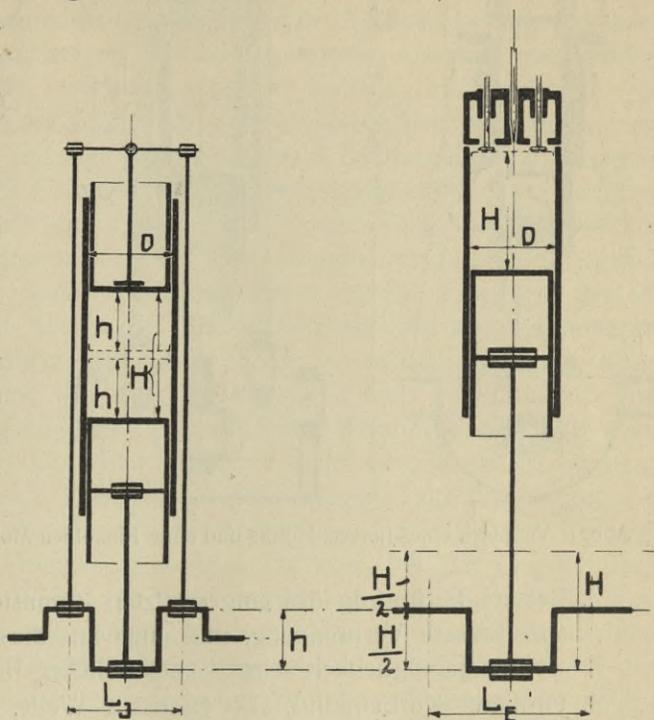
Maschinen mit gleichem Hubverhältnis (D:H) links Gegenkolbenmaschine, rechts Einkolbenmaschine. Die Gegenkolbenmaschine beansprucht weniger Platz.
